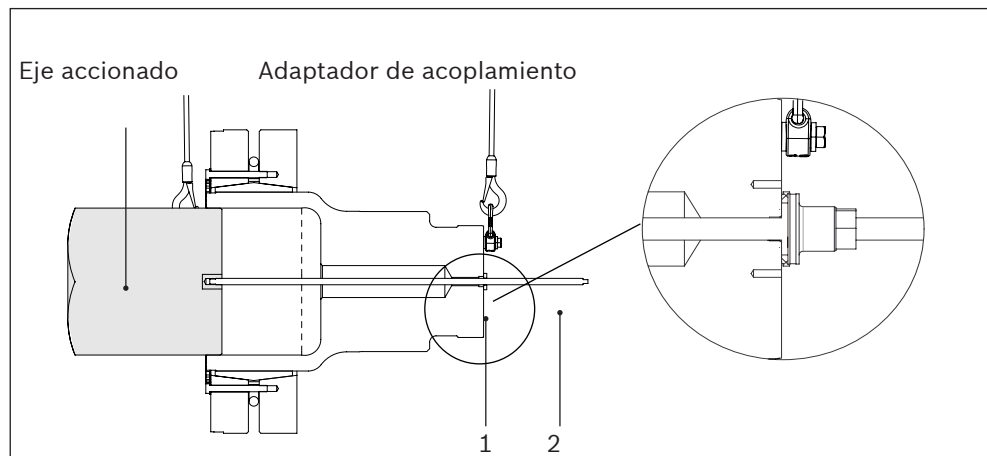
Instalación del adaptador de acoplamiento en el eje accionado con la herramienta de montaje.
